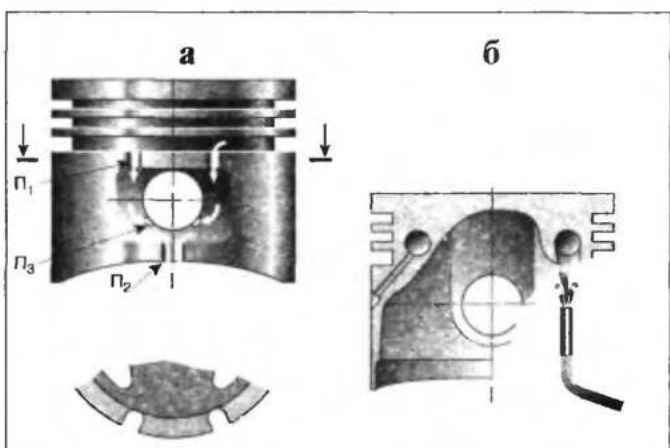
Способы улучшения смазки поршня, колец и цилиндра: а — сбросом масла из канавки маслосъемного кольца в холодильник; П1 — паз из канавки в холодильнике; П2 — паз из холодильника; П3 — пазы вдоль отверстия пальца для его смазки; б — подачи масла на поверхность юбки из полости масляного охлаждения поршня
